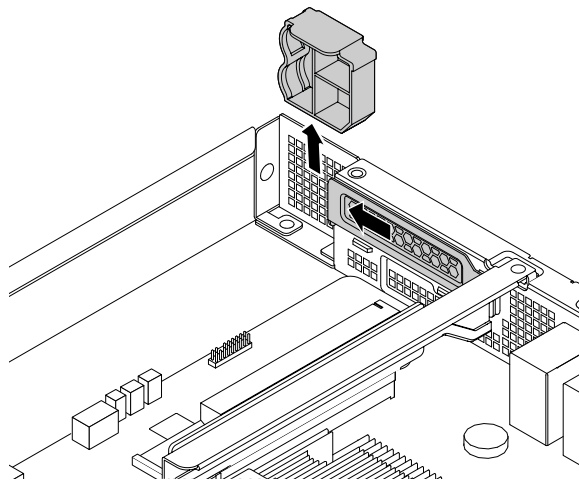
PCIe-Steckplatzhalterung entfernen
